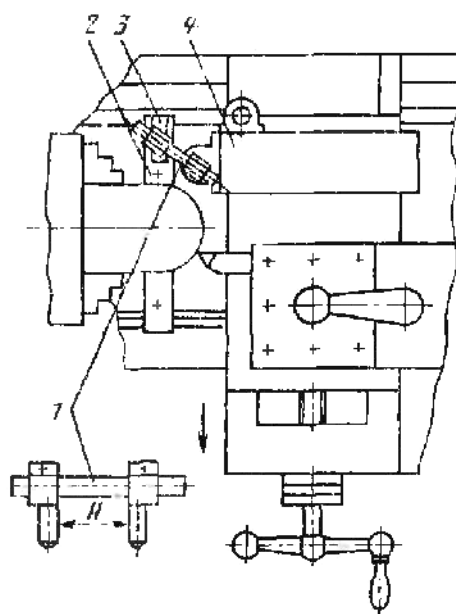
Приспособление шарнирно-стержневого типа
